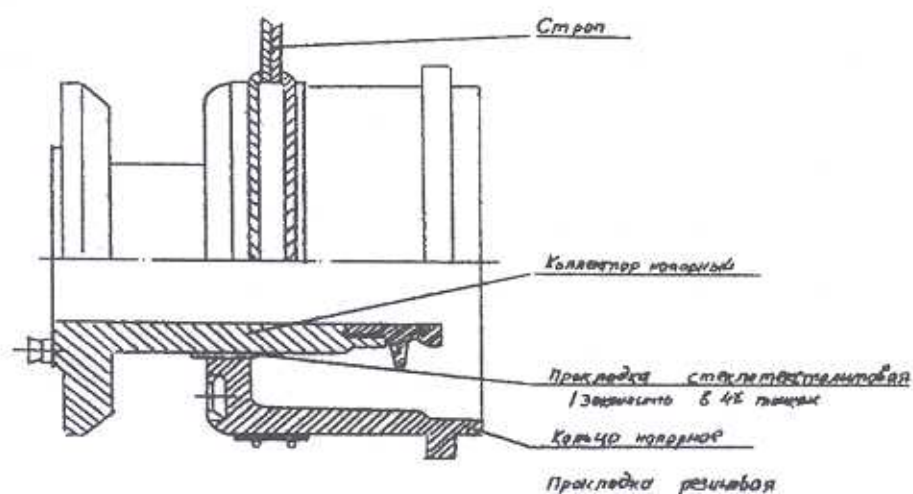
Схема строповки узла «напорное кольцо-напорный коллектор»
